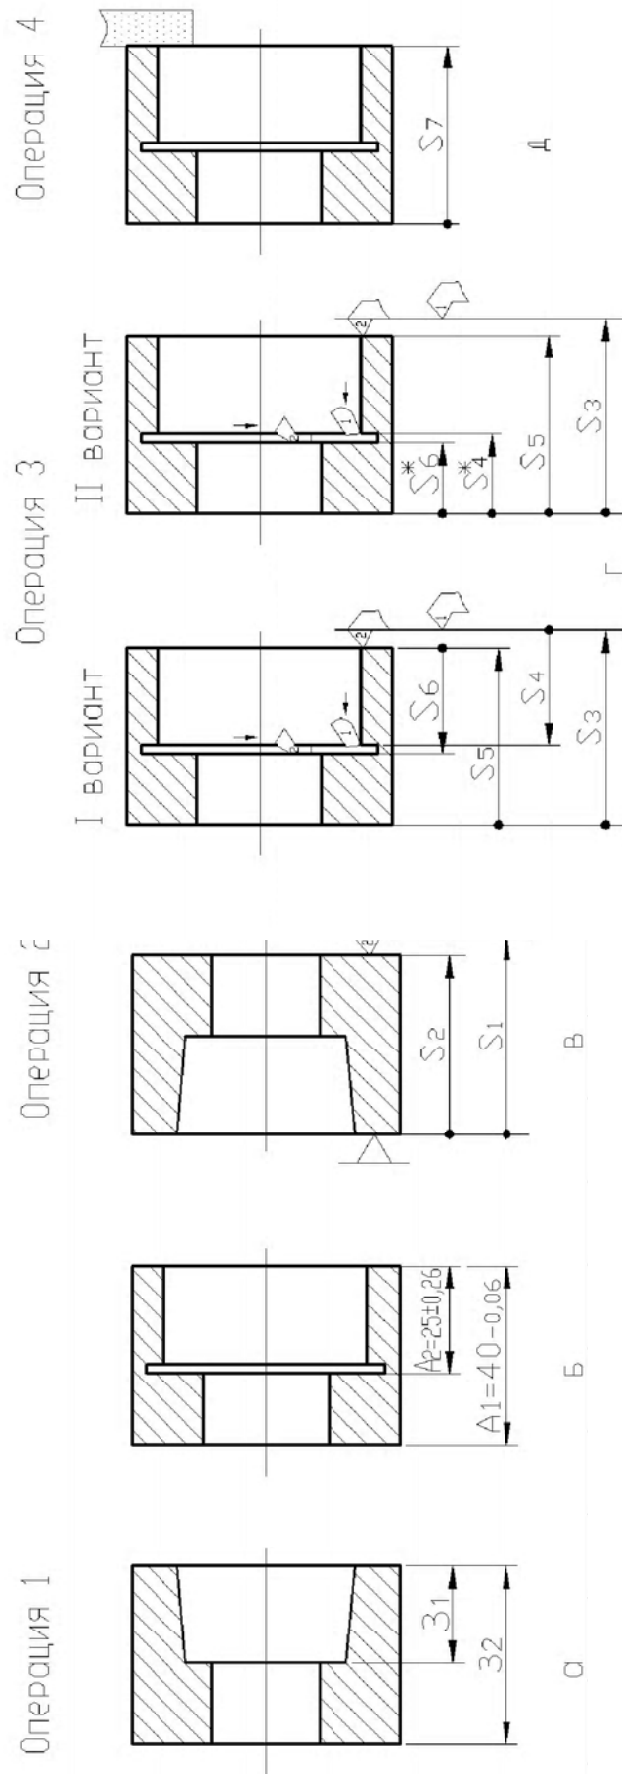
Втулка: а – эскиз заготовки; б – эскиз детали; в, г, д – операционные эскизы изготовления втулки
